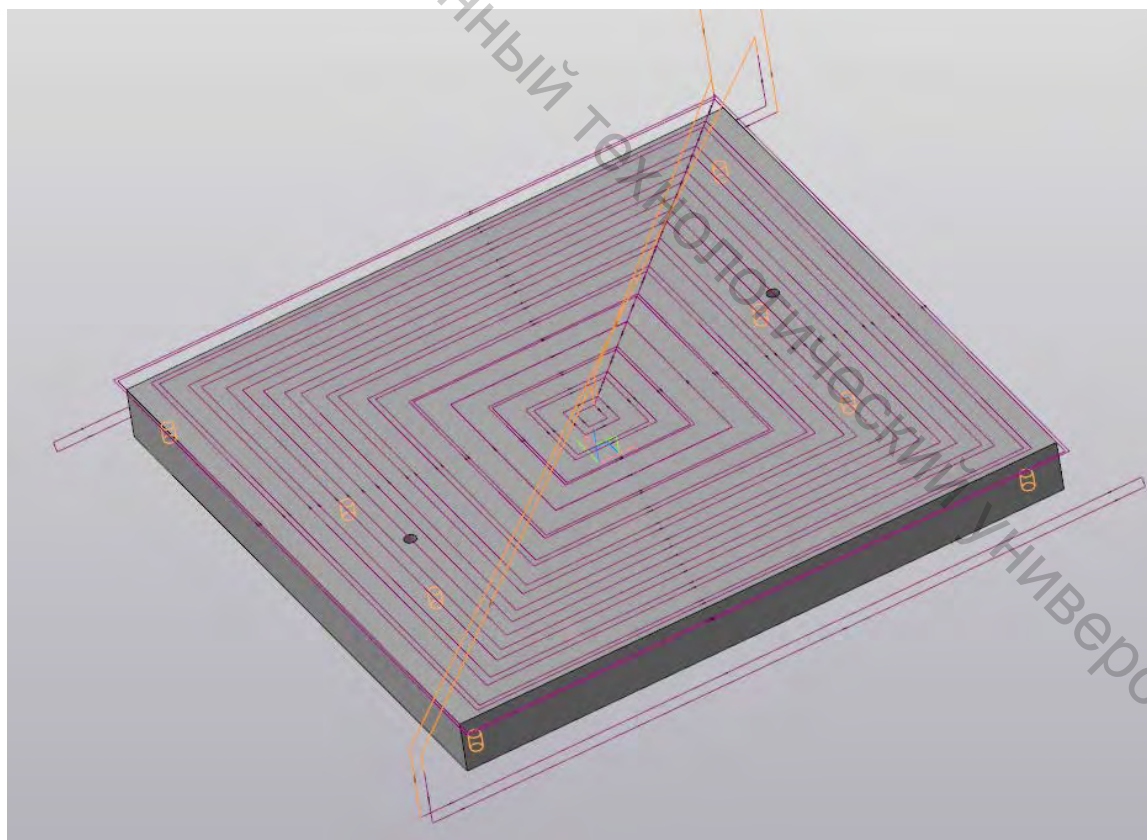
Траектория инструмента при черновом и чистовом фрезеровании заготовки во втором установе
